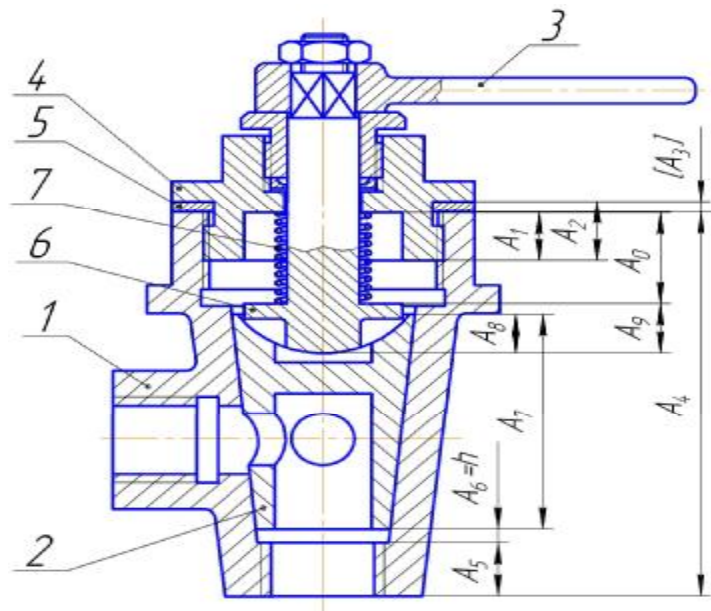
Сборочный чертеж двухходового крана и его СРЦ
